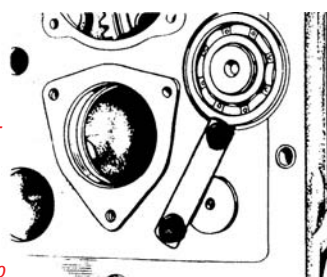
Выпрессовка промежуточного вала, замена ведущей шестерни I ступени редуктора, промежуточной шестерни, ведомых шестерен 4, 3, 5-й
